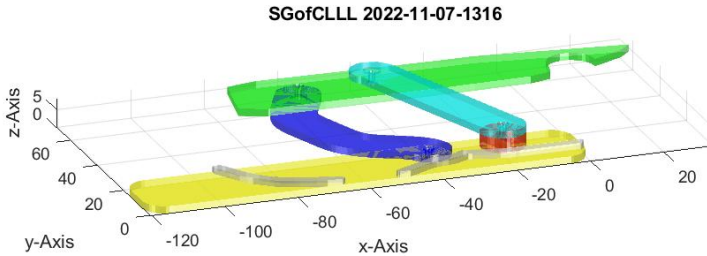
3D-Ansicht der Baugruppe für eine einfachere Montage
